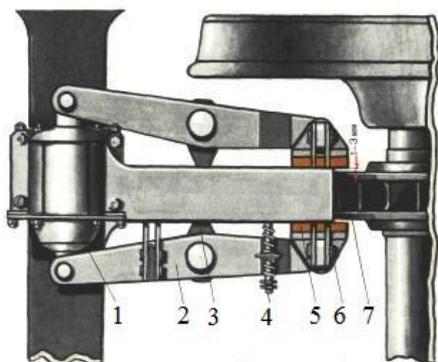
Дисковый тормоз (вид сверху):
